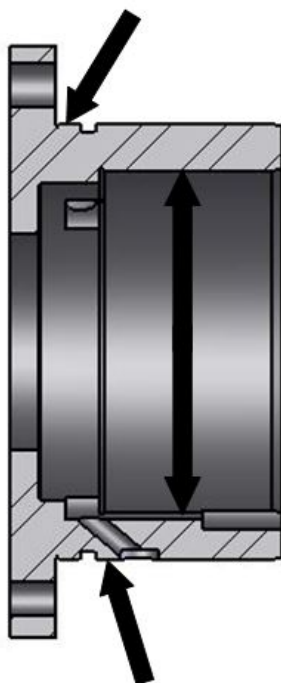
Áreas de inspección - Grupo 3 de la caja de rodamientos
